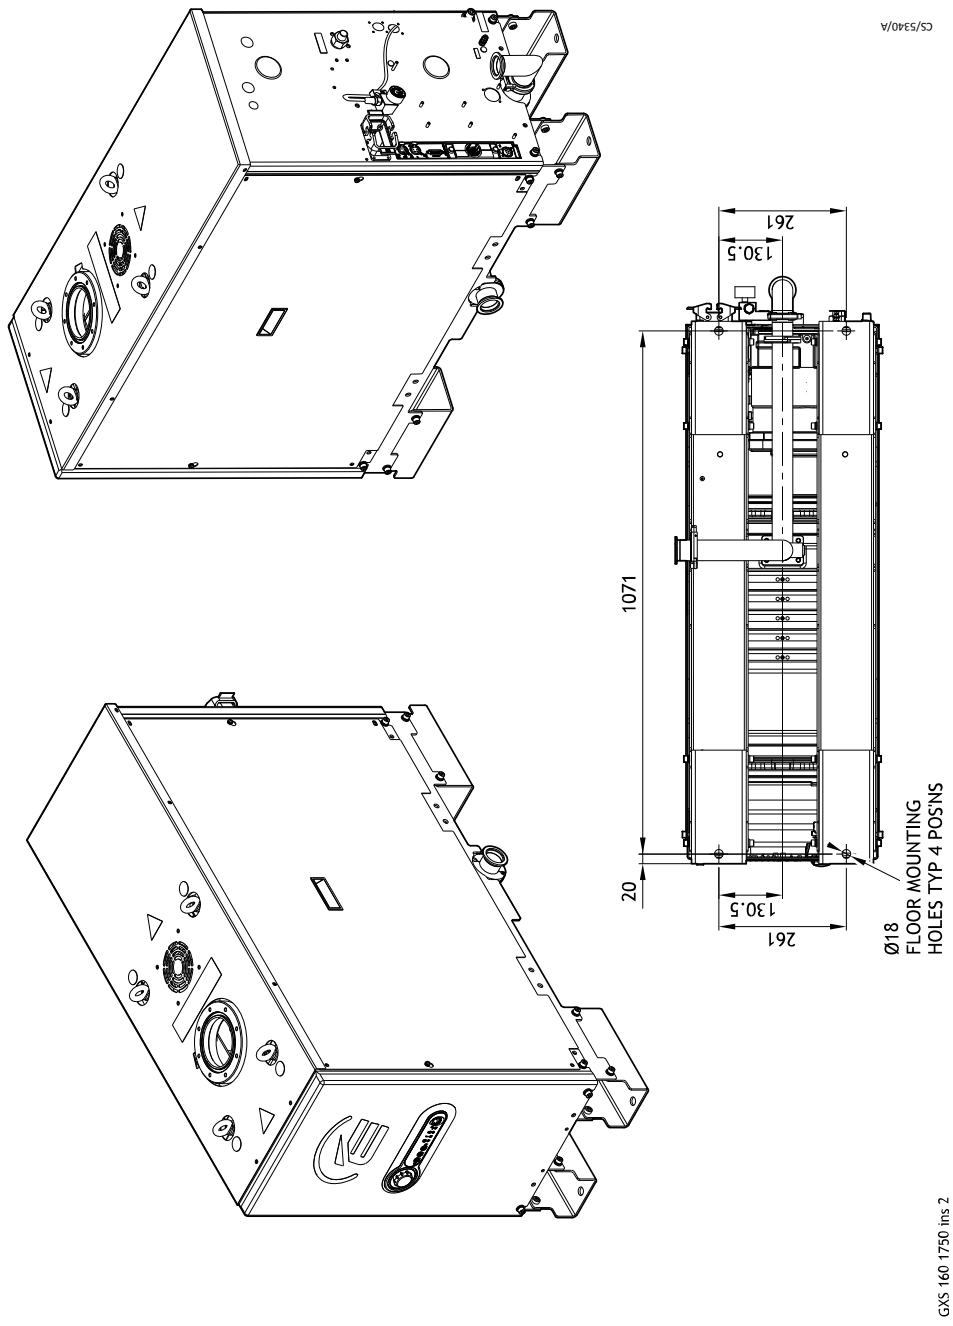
GXS160/1750 Installationszeichnung (Blatt 3)
